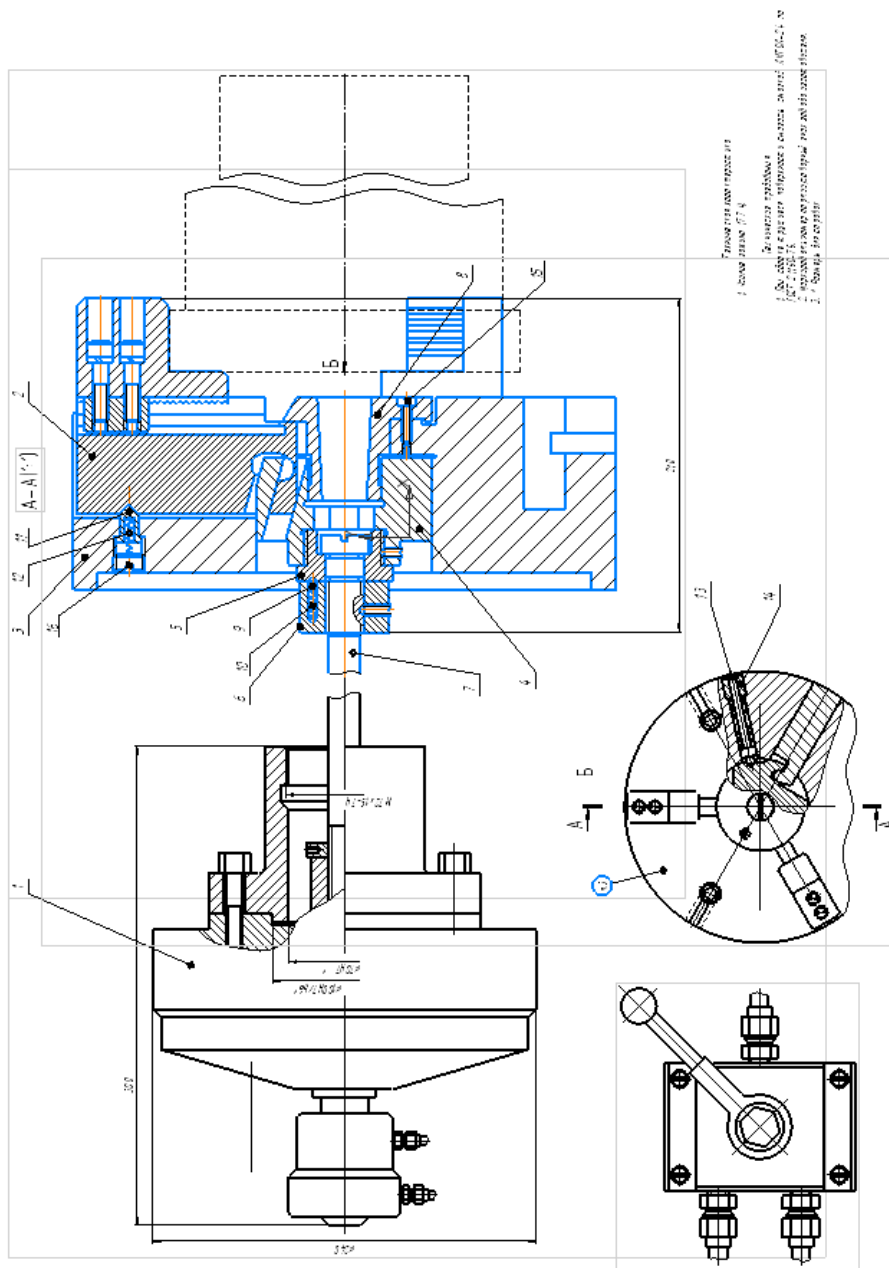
Чертеж станочного приспособления «Трехкулачковый патрон с пневматическим зажимом»
